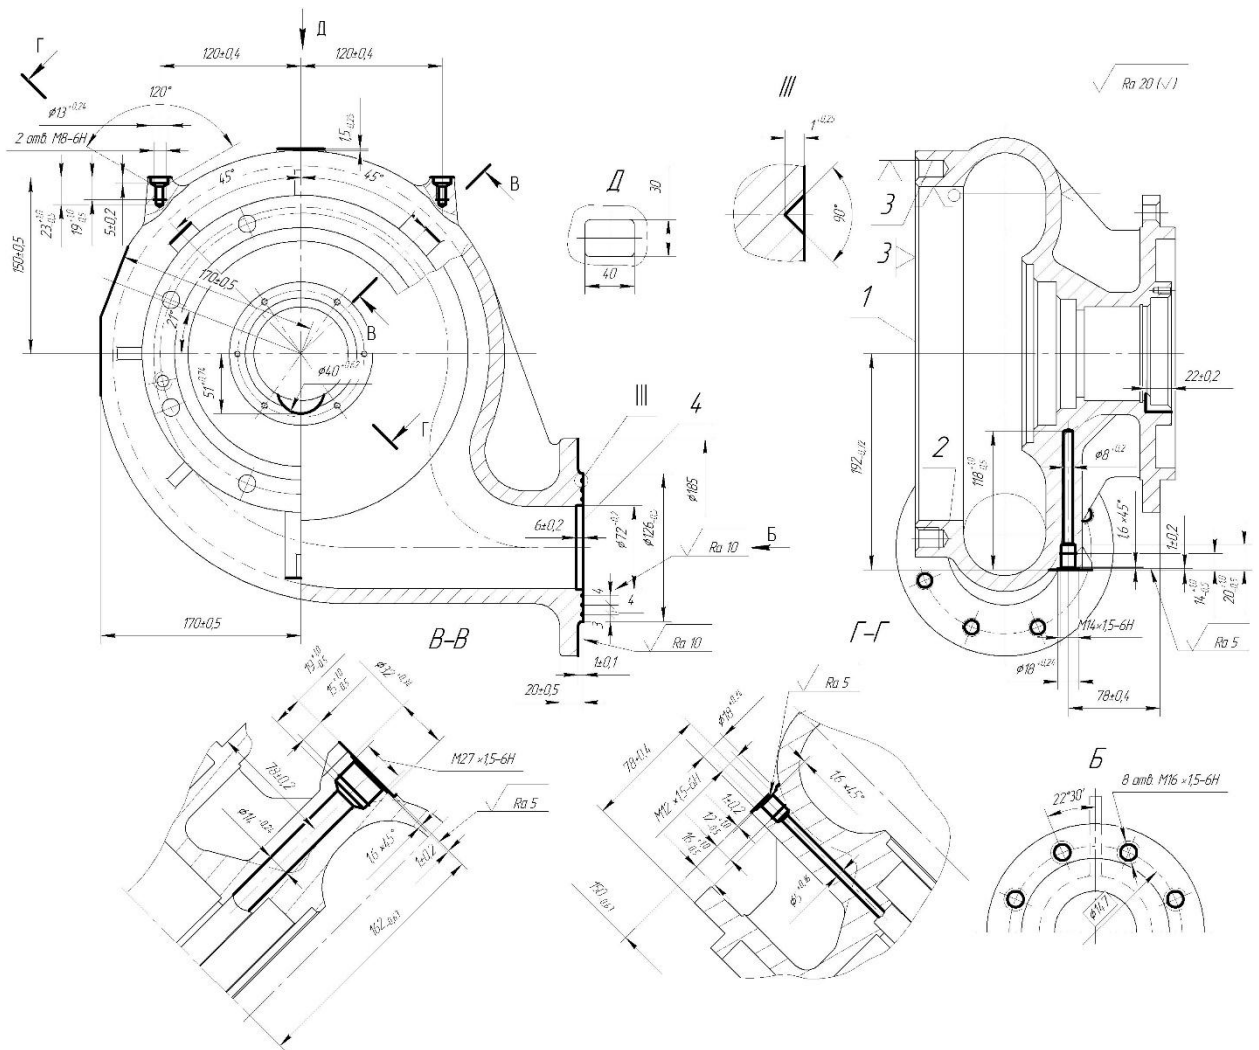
Ескіз механічної обробки деталі на свердлильно-фрезерно-розточну операцію
